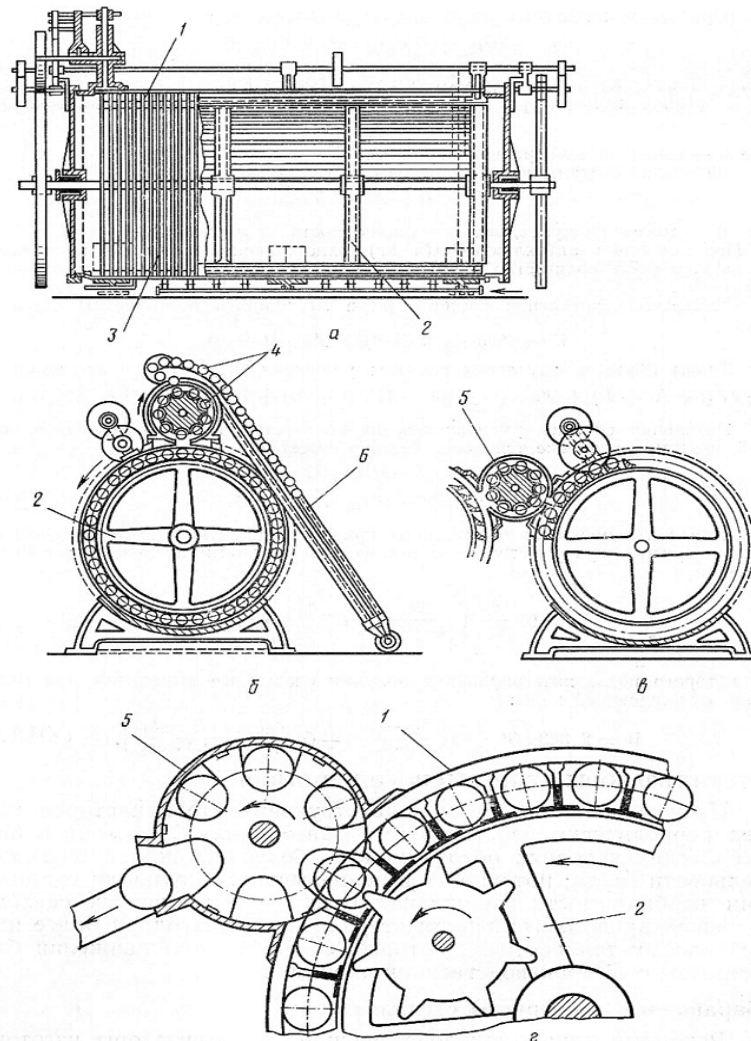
Барабанний (роторний) стерилізатор безперервної дії: 1 - корпус; 2 - барабан; 3 - спіральна направляюча; 4, 5 - відповідно завантажувальний і розвантажувальний пристрій; 6 - ланцюговий елеватор.
